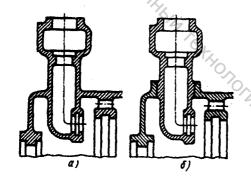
Цельнолитая и сварно-литая конструкции
